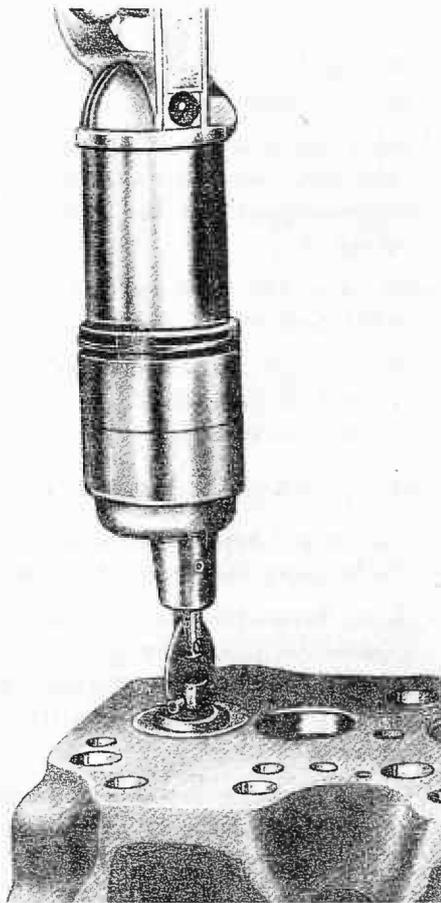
Anwendung der Ventil-Einschleifmaschine
